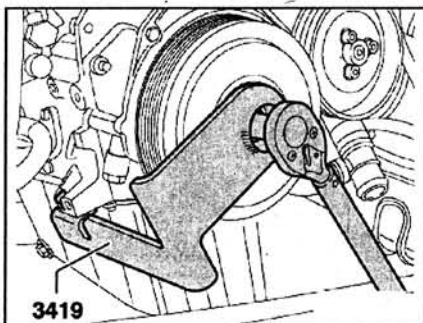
Установите стойку 3419 или T10025 и ослабьте центральный болт крепления канавочного и зубчатого шкивов коленчатого вала.
